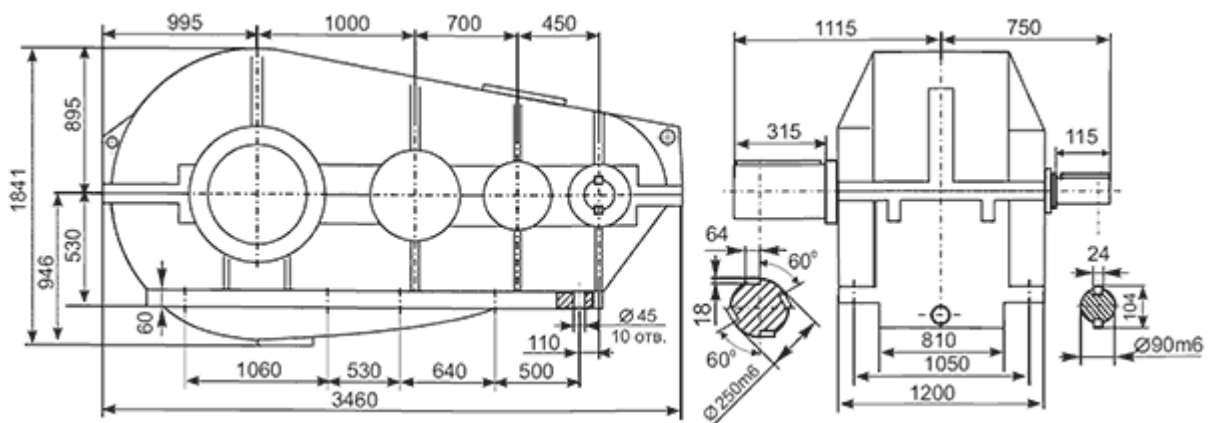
Креслення редуктора РЦТ-2150-8-М
